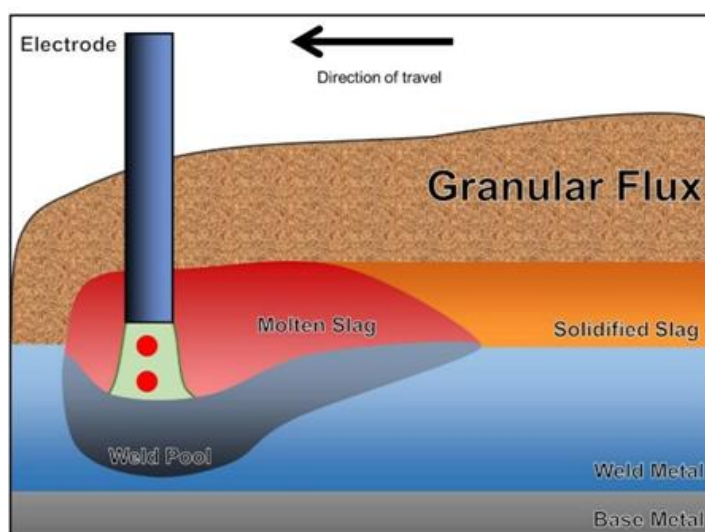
Схема автоматичного зварювання під шаром флюсу [5]
